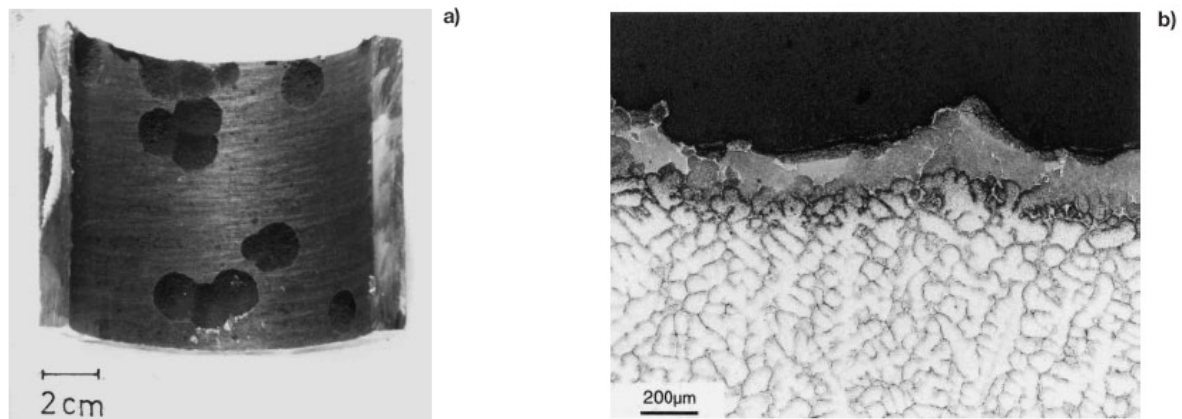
Ataque del Metal dusting en un tubo de calentador de una planta de reducción directa a 600 °C [22]. a) Sección de un tubo de HK40 con picaduras profundas, b) Sección transversal que muestra la zona carburizada.
